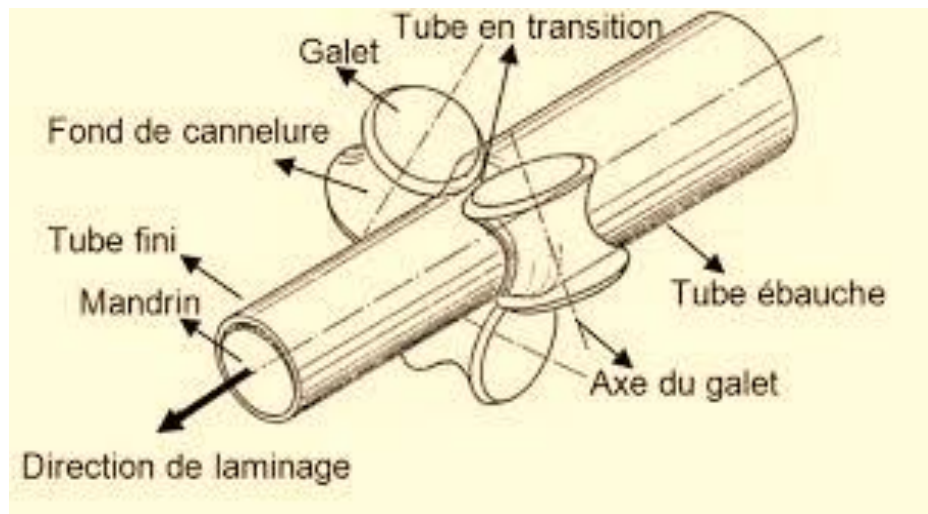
Fabrication des tubes sans soudures [33].
